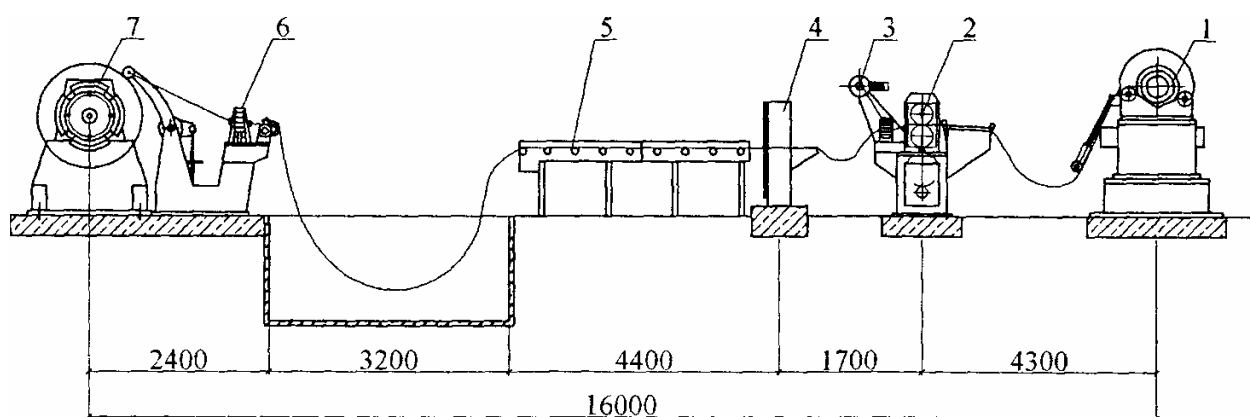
Лінія поздовжньо-поперечного розпуску рулону: 1 - розмотувач стійковий; 2 - ножиці дискові; 3 - крайконамотувач; 4 - гільйотина поперечна; 5 - стіл-штабелер; 6 - правильно-натяжний пристрій; 7 - консольний пристрій, що намотує штрипс
